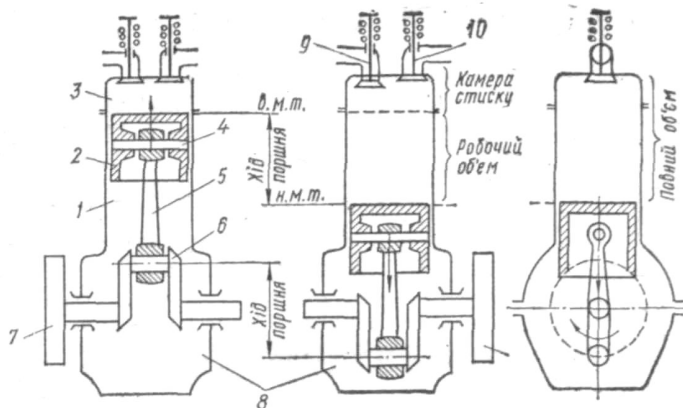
Схема двигуна внутрішнього згоряння: 1 – циліндр; 2 – поршень; 3 – головка циліндра; 4 – поршневий палець; 5 – шатун; 6 – колінчастий вал; 7 – маховик; 8 – картер; 9 – впускний клапан; 10 – випускний клапан
